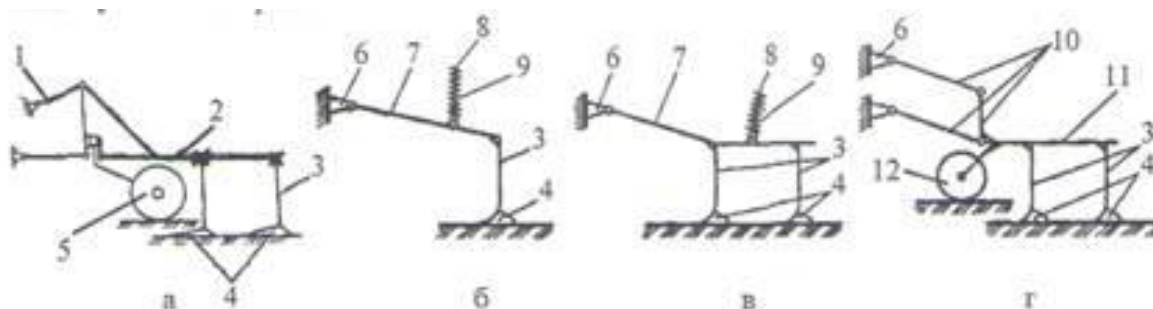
Схеми кріплення робочих органів культиватора Strip-till
